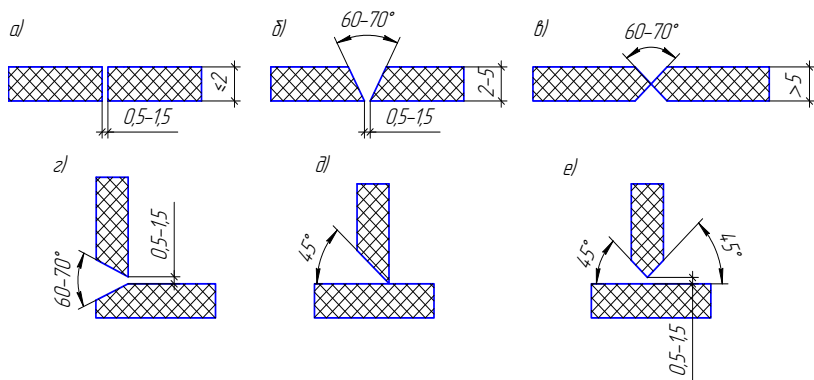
Подготовка кромок деталей перед сваркой: *a* – без разделки кромок; *б, в* – соответственно с V- и X-образной разделкой; *з* – разделка кромок углового соединения; *д, е* – то же, для таврового соединения
